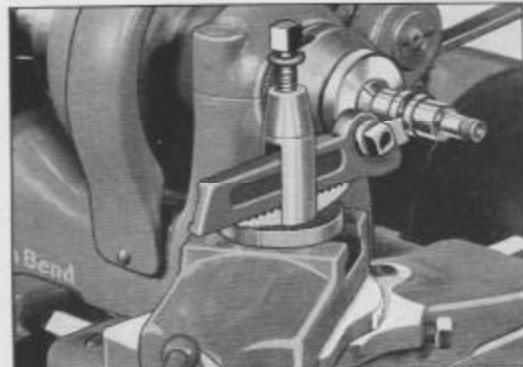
Usinage d'une Pièce tenue par un Dispositif de Serrage à Pincés Américaines
